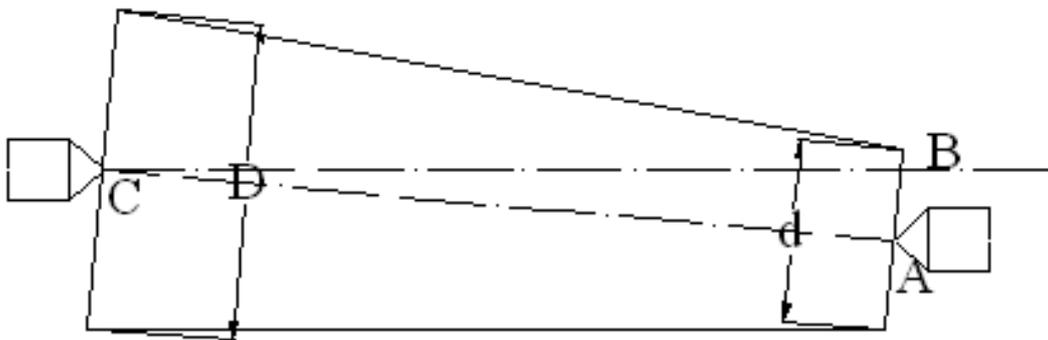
Construcción cónica por desplazamiento del contrapunto
